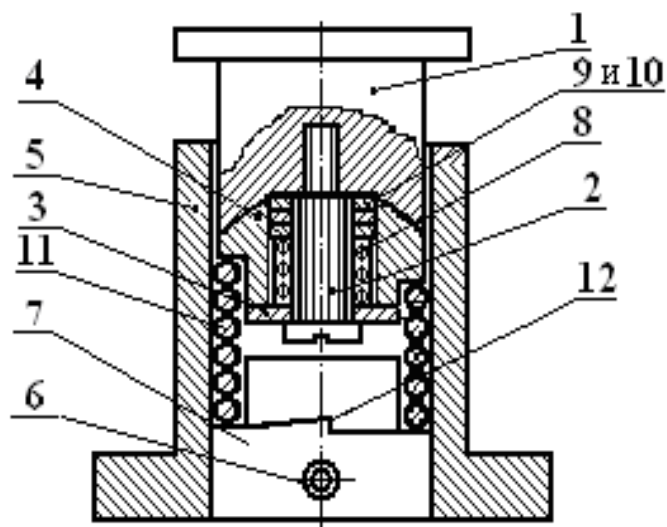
Устройство для заневоливания пружин по пат. RU 2390667 [100]
